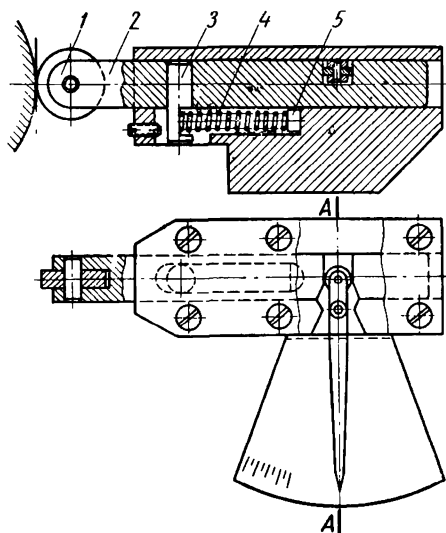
Секторный индикатор для измерения поковок; цена деления 0,2 мм; диапазон измерения  $\pm 5$  мм: 1 — ролик; 2 — измерительный шток; 3 — поводок; 4 — пружина; 5 — упор; 6 — корпус индикатора; 7 — крышка; 8 — ролик стрелки; 9 — стрелка; 10 — секторный циферблат
